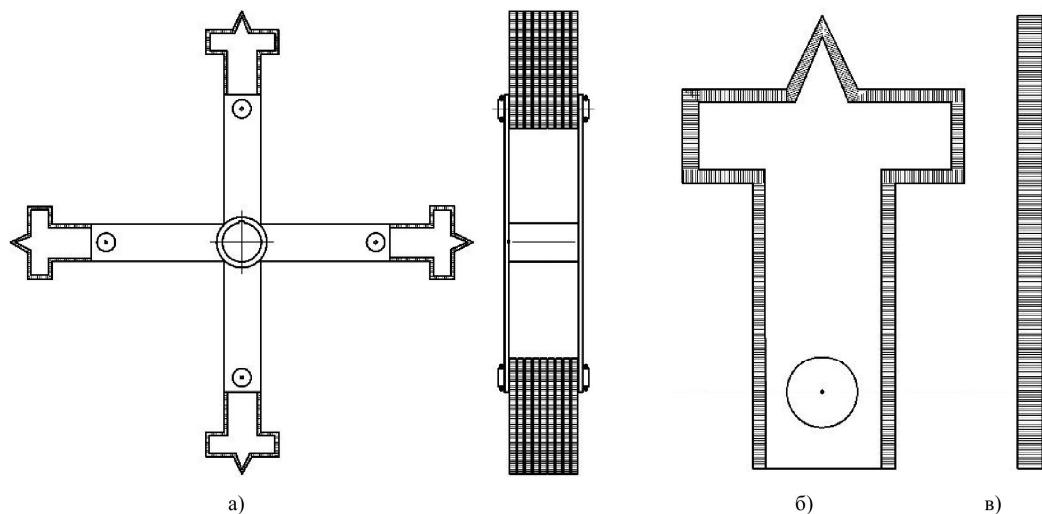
Молотки малогабаритної зернової кормодробарки;
